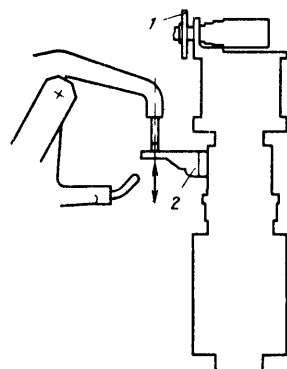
Дополнительное оборудование сварочной ячейки:
